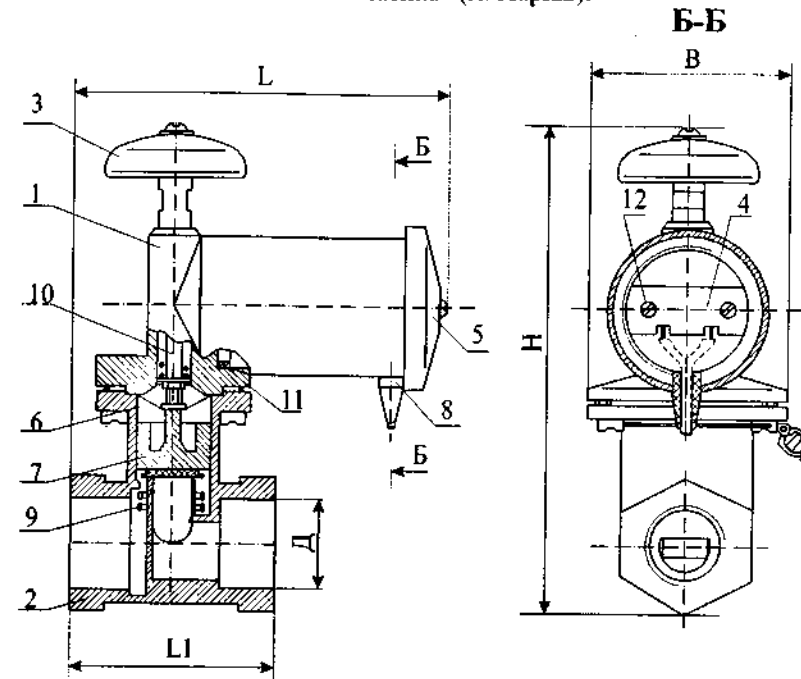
Загальний вигляд клапанів типу КЭИ-1-15/12 (20/12, 20, 25/12, 25/20, 32/20): 1, 2- верхній і нижній корпуси; 3- рукоятка; 4 - з'єднувальна колодка; 5- кришка; 6 - мембрана; 7 - заслінка; 8 - гумова прохідна втулка; 9 пружина; 10 тяга; 11 кільце; 12 гвинти.
